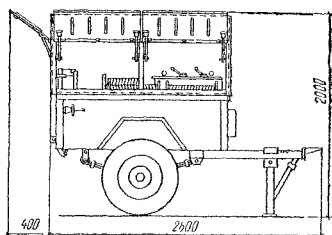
Машина МТП-25 для контактной точечной сварки
